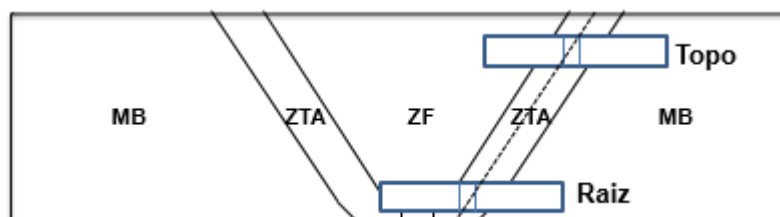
Representação esquemática de uma junta soldada com direção do entalhe para teste Charpy na ZTA.
